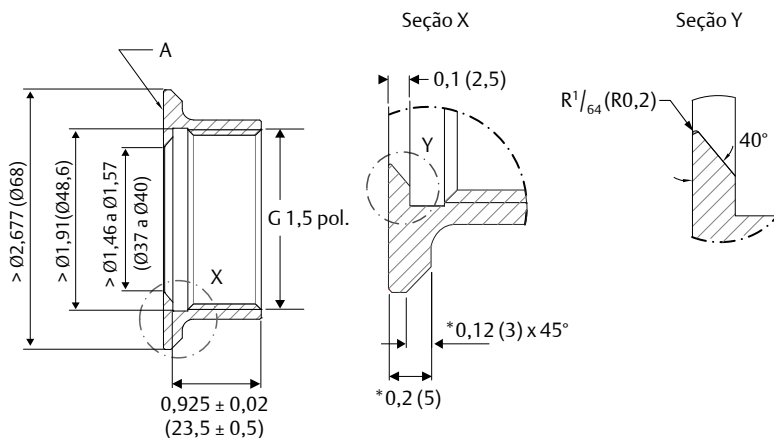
Vedação de metal-metal usando soquete soldado
